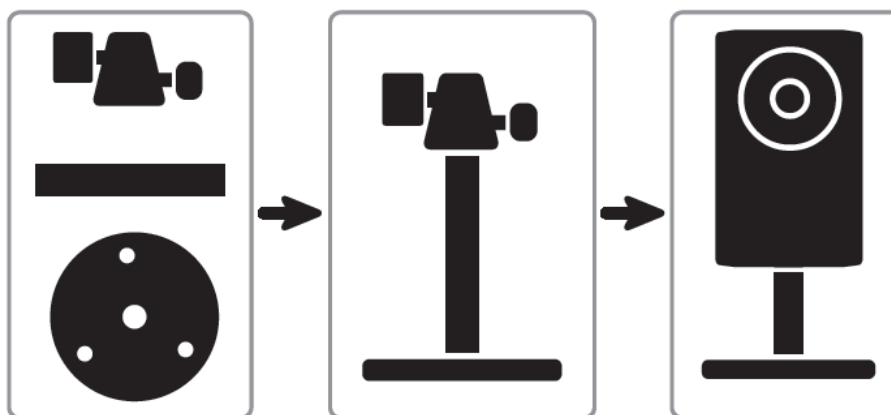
Схема сборки камеры LTV-ICCM1-B320-F3.8
